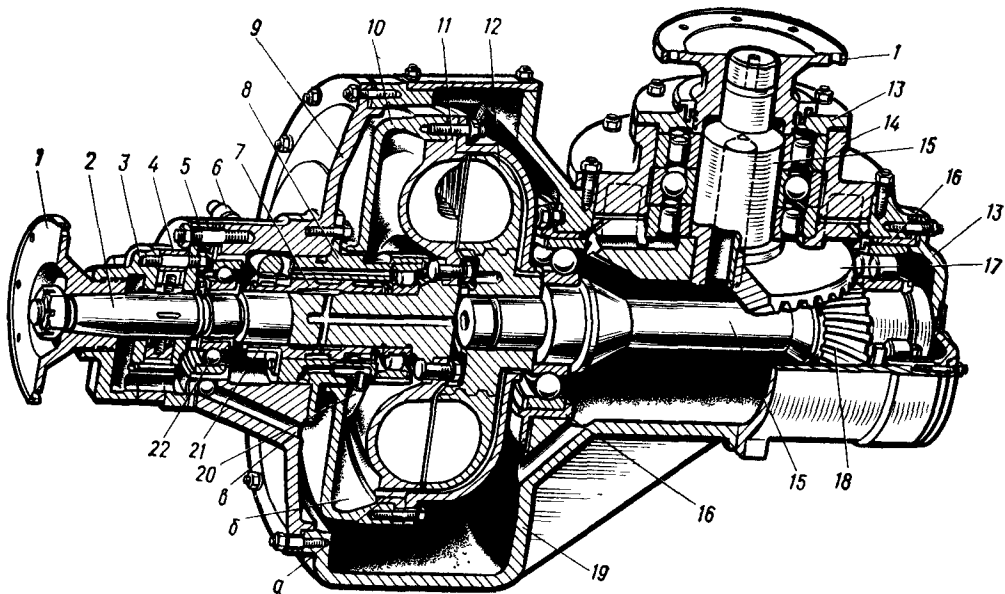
Гидромуфта переменного наполнения с редуктором:
